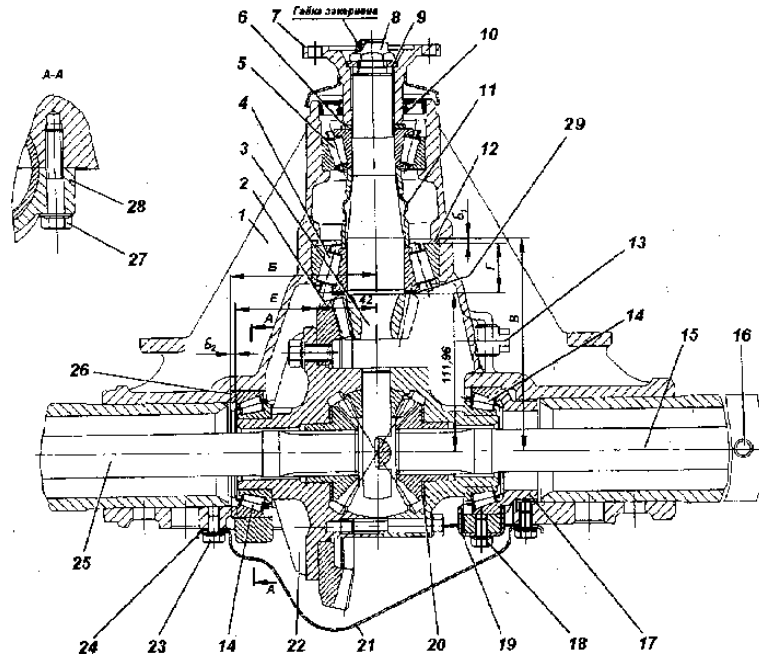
Мост задний: 1 -картер; 2 -шестерня ведомая главной передачи; 3 -шестерня ведущая главной передачи; 4 -подшипник задний; 5 -подшипник передний; б -кольцо; 7 -фланец; 8 -гайка; 9 -шайба; 10 -манжета; II -втулка распорная; 12 -кольцо регулировочное; 13- пробка заливного отверстия; 14-подшипник дифференциала; 15 -полуось правая; 16 -клапан предохранительный; 17 -гайка подшипника дифференциала; 18 -болт; 19 -пластина стопорная; 20 -шайба упорная; 21 -крышка картера; 22 -дифференциал; 23 -болт; 24 -прокладка; 25 -полуось левая; 26 -кольцо регулировочное; 27 -болт; 28 -крышка подшипника дифференциала; 29 -маслоотгонное кольцо
